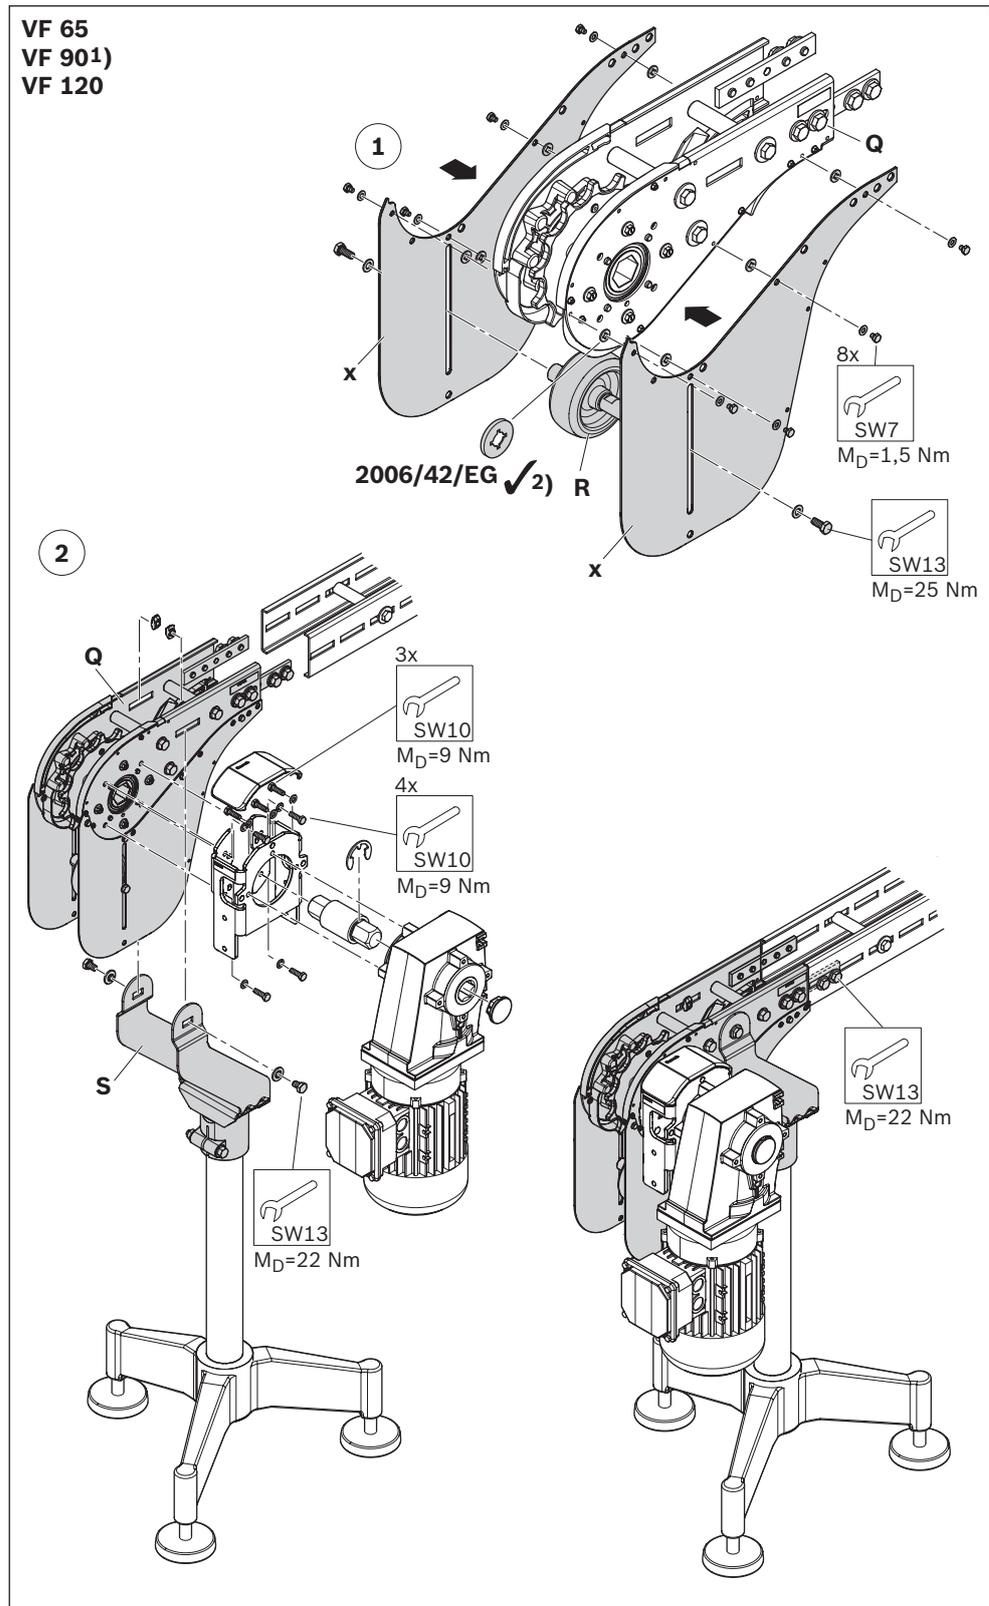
Sistema STS, montaje de la unidad básica, VF 65/VF 90/VF 120
